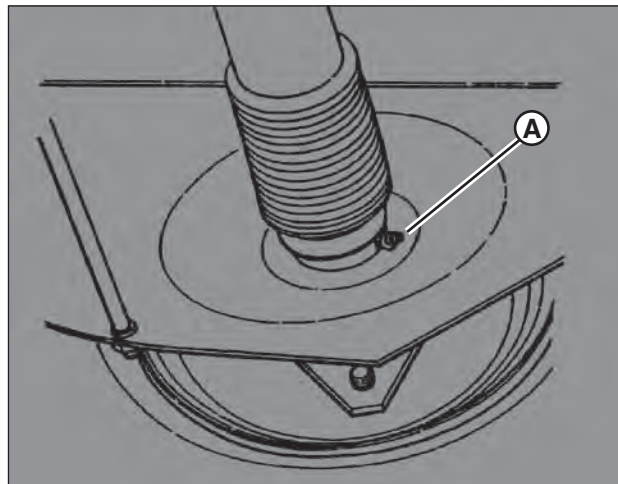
Graisseur d'essieu arrière (vue du dessous de la machine)
